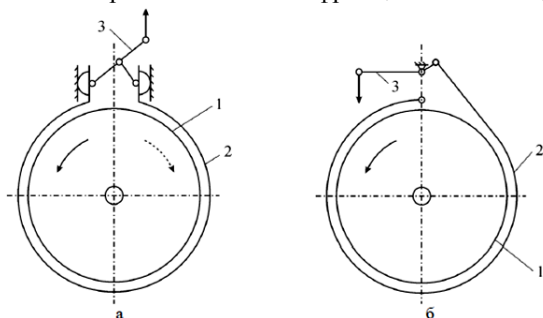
Схема ленточного тормоза: а – с плавающим креплением ленты; б – с неподвижным креплением ленты; 1 – тормозной шкив; 2 – тормозная лента; 3 – рычаг
